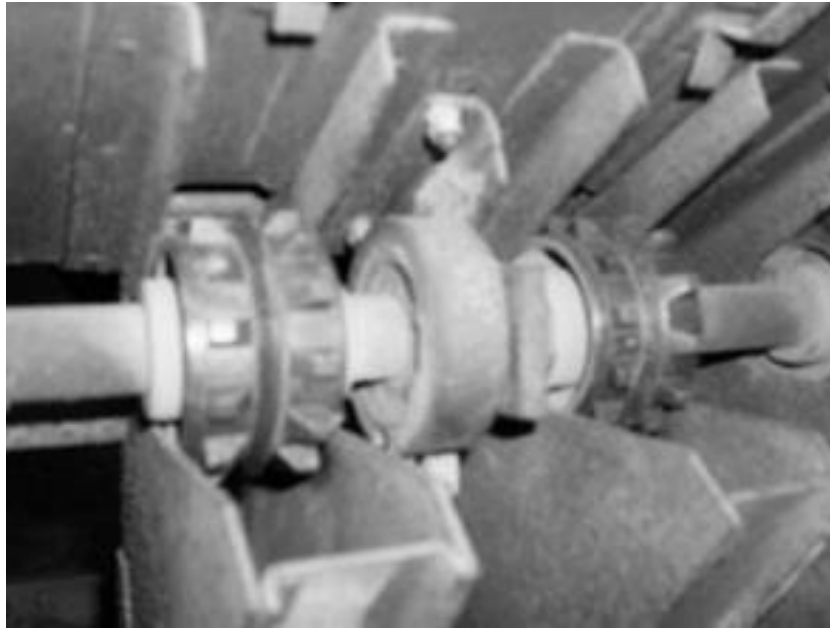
Загальний вигляд переобладнаного ВВА для установки САУВН
